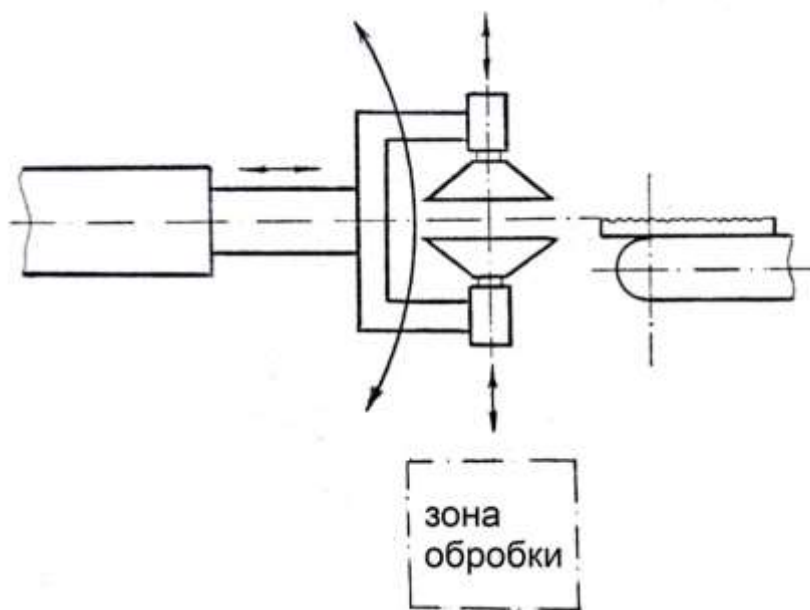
Схема руки промислового робота з чутливим захватом для подачі на обробку деталей з різною шорсткістю поверхонь
